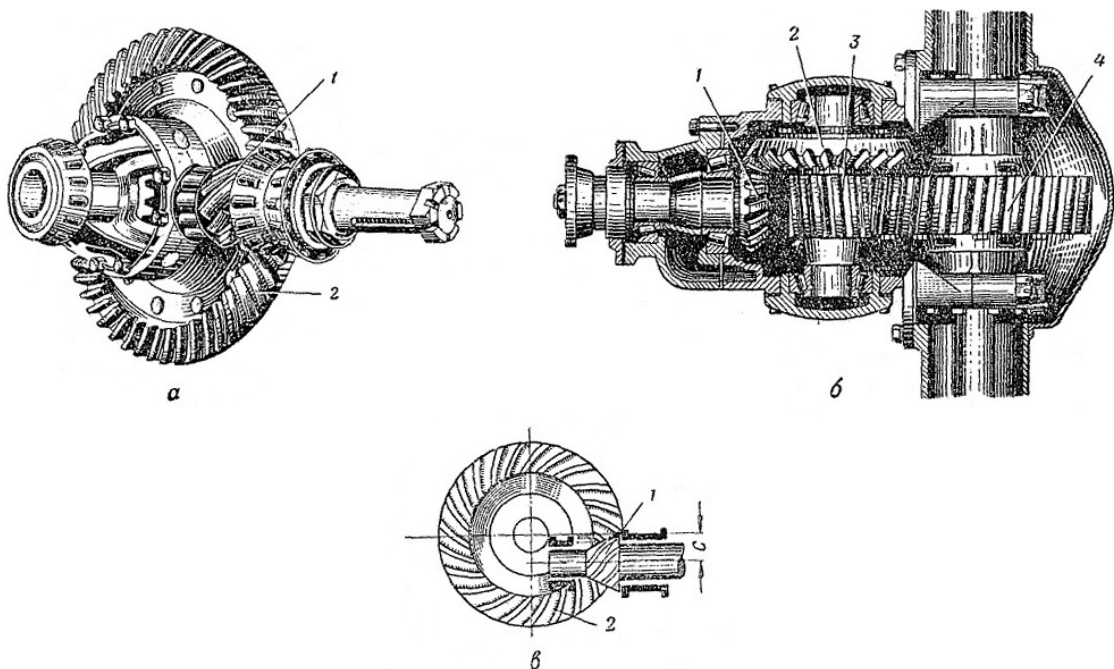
Главные передачи: а — одинарная; б — двойная; в — одинарная гипоидная; 1 — ведущая коническая шестерня; 2 — ведомая коническая шестерня; 3 — малая цилиндрическая шестерня; 4 — большая цилиндрическая шестерня
